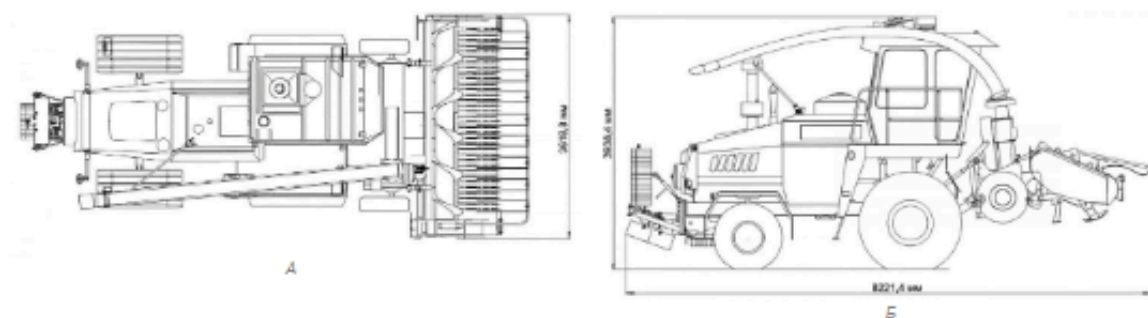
А – вид сверху, Б – вид сбоку. Габаритные размеры энергосредств в агрегате с комбайном, с подборщиком.
